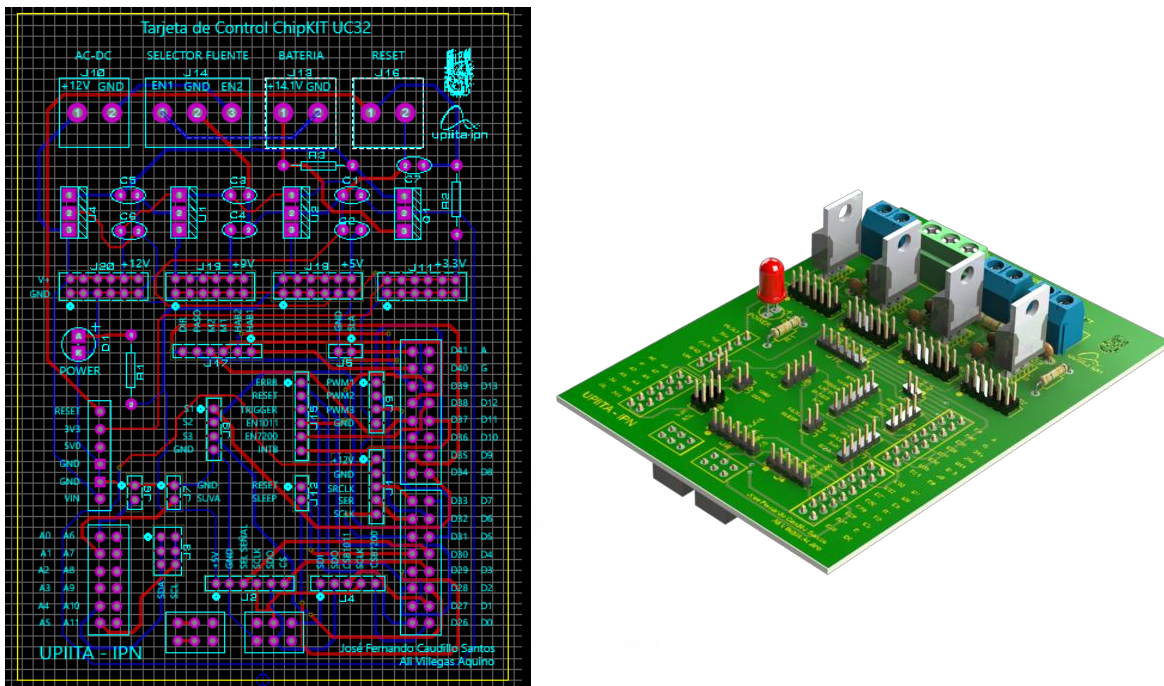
Diseño del PCB y Modelo en 3D de la Tarjeta de Control.
